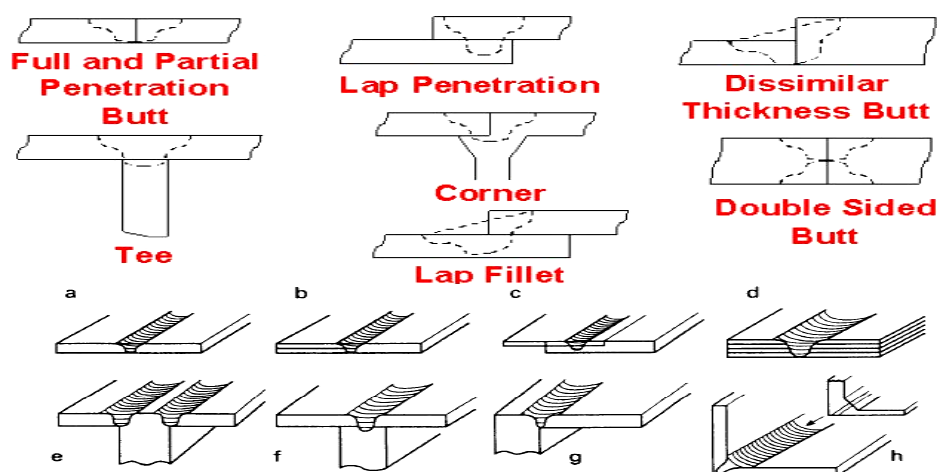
Juntas de Soldadura ou tipologias típicas para SFL.
